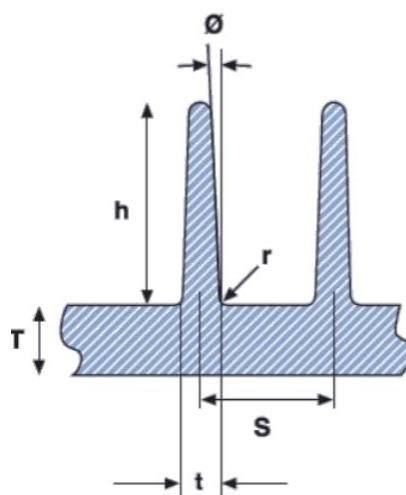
Pravilno oblikovanje rebraste ukrute [5]
